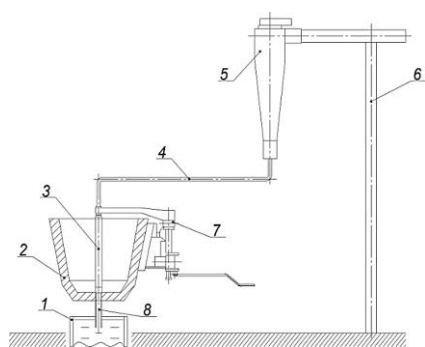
Конструктивная схема установки для вдувания газопорошковых смесей через стопорный разливочный узел промежуточного ковша МНЛЗ
